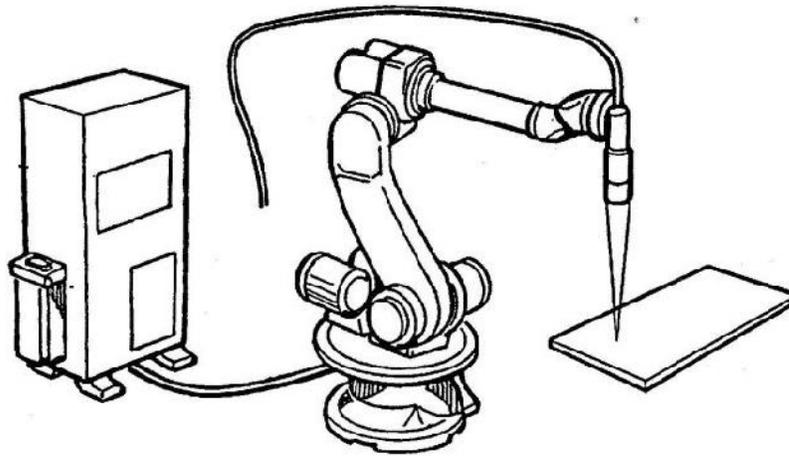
Equipo empleado en la soldadura robótica.
